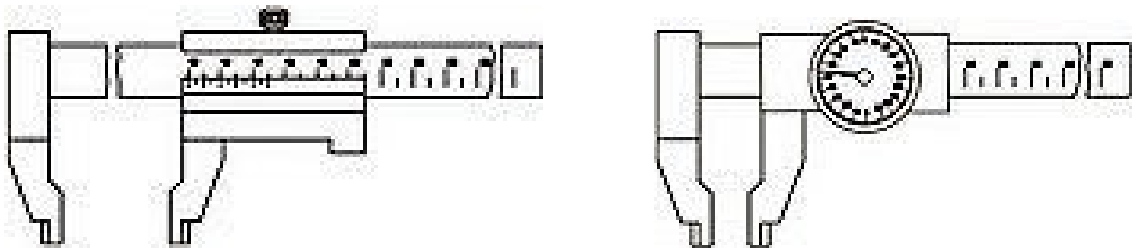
Штангенциркуль ШЦ-III-125-0,05 [ГОСТ 166-89]
